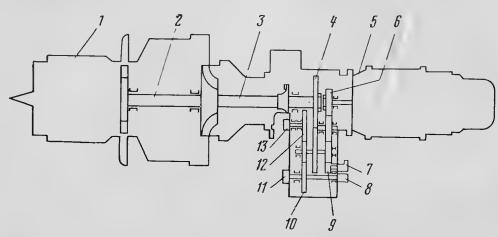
Кинематическая схема турбогенераторной установки ТГ-16: 1—газотурбинный двигатель; 2—ротор двигателя; 3—ведущий вал редуктора; 4—ведущая шестерня; 5—генератор ГС-24А; 6—шестерня привода генератора; 7—датчик тахометра; 8—ограничитель максимального числа оборотов; 9—шестерня привода датчика тахометра; 10—шестерня привода насосарегулятора ТНР-3РА; 11—насос ТНР-3РА; 12—шестерня привода маслоагрегулятора ТНР-3РА; 11—маслоагрегат
